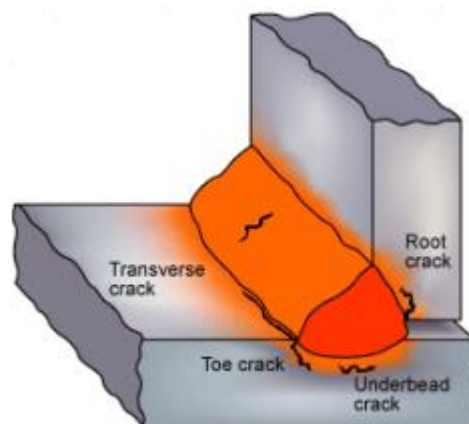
Tipologia e localização das fissuras a frio.[11]
